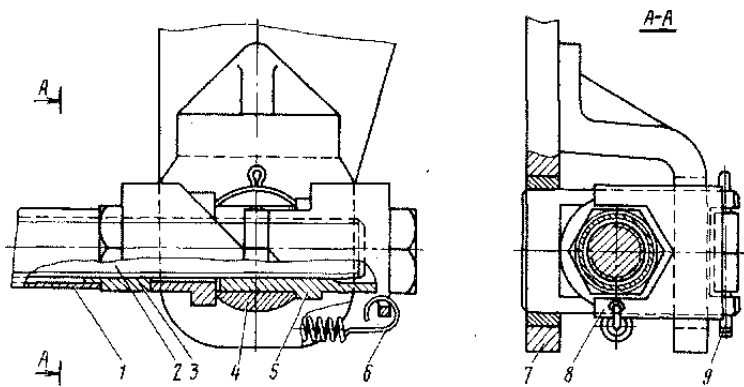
Регулятор выхода штока тормозного цилиндра: 1 - защитная труба; 2 - тяга; 3 - втулка; 4 - палец; 5 - гайка; 6 - пружина; 7 - рычаг, 8 - скоба; 9 - шплинт
